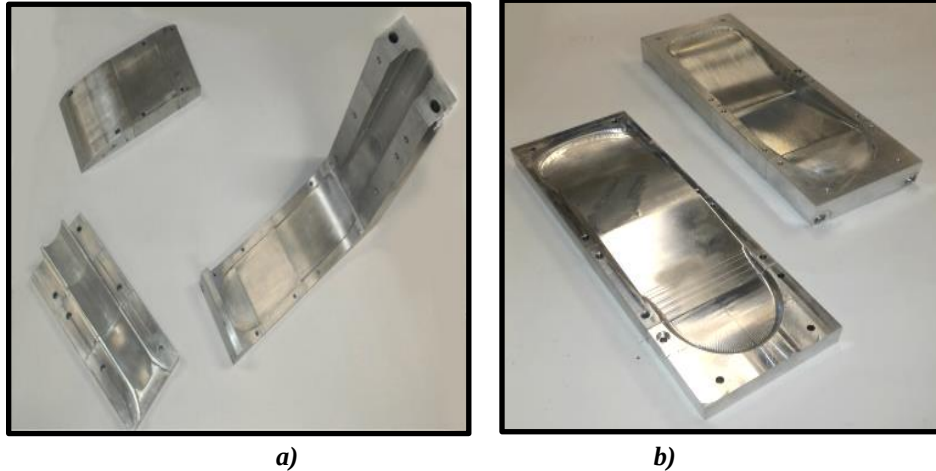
Segundo molde en aluminio: a) Pieza superior; b) Pieza inferior.
